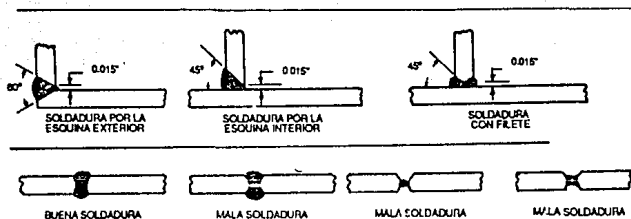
Uniones para la soldadura por gas. (Ref. 2)
